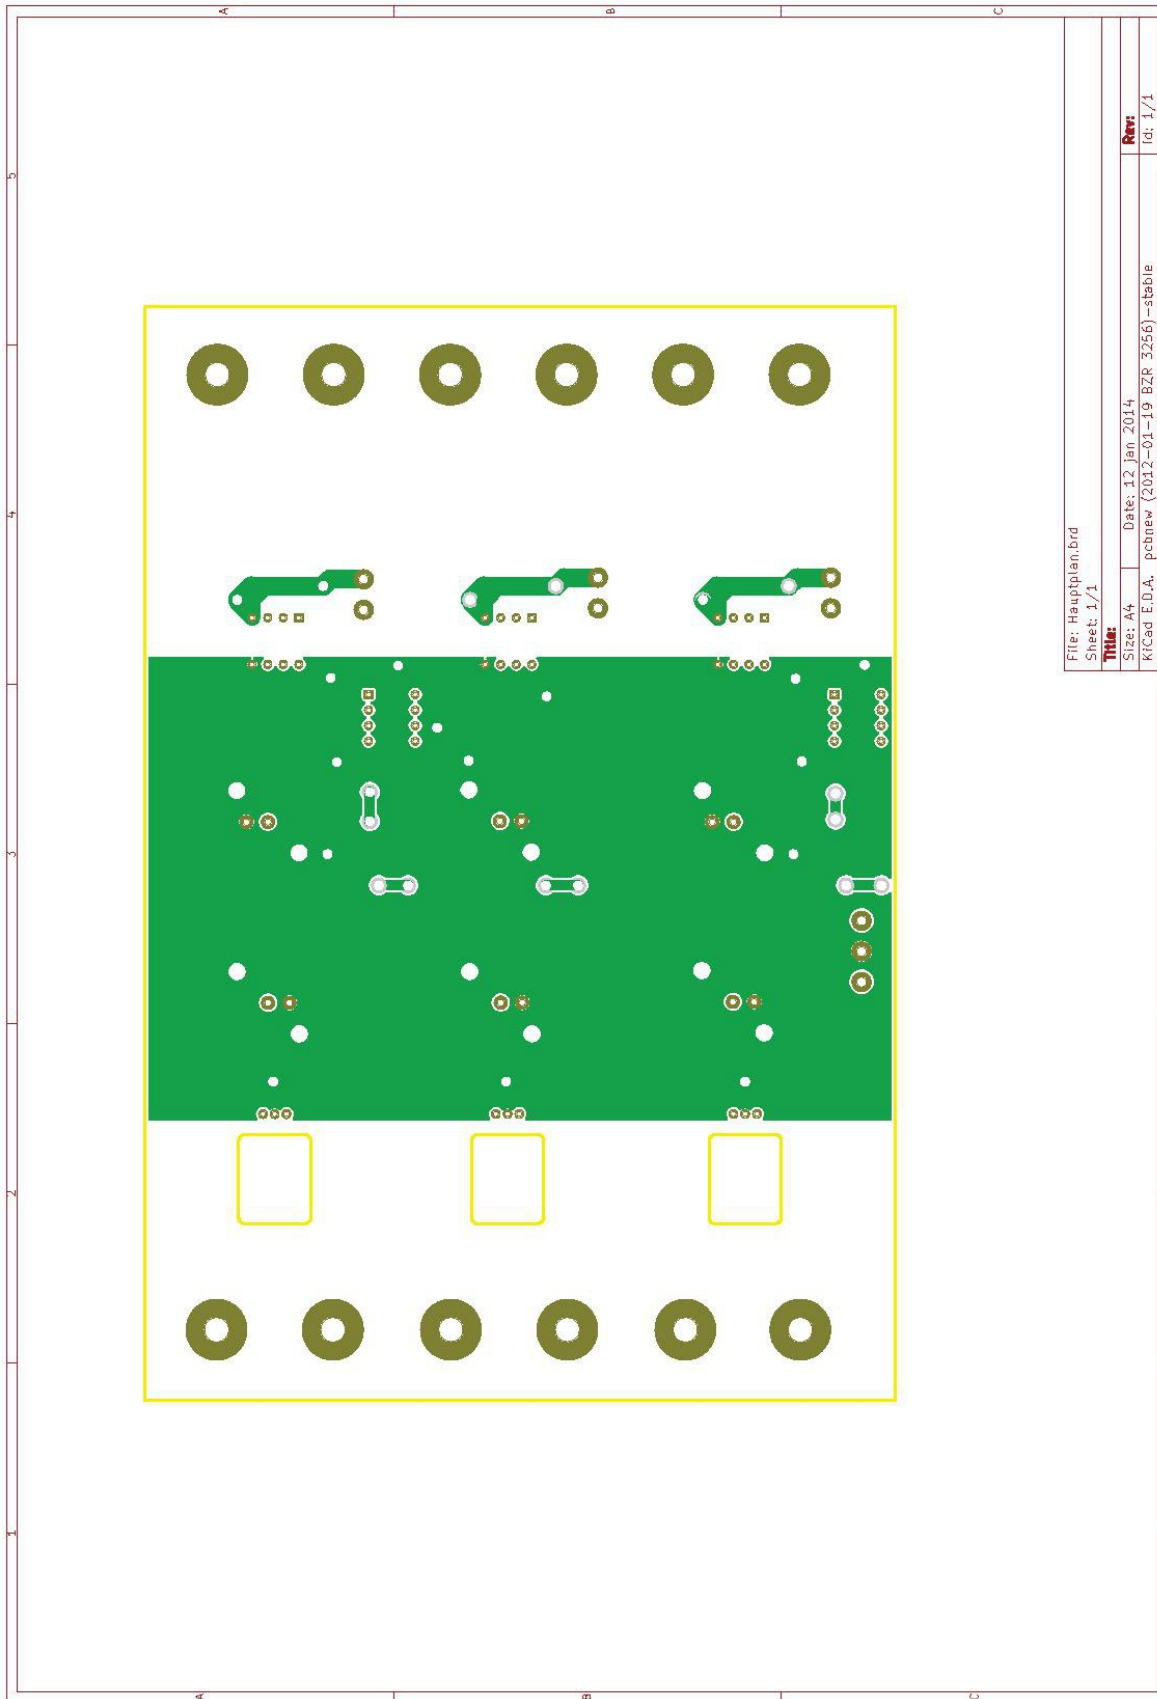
PCB-Layout Rückseite (bottom) der Gruppierungen 1 und 2
